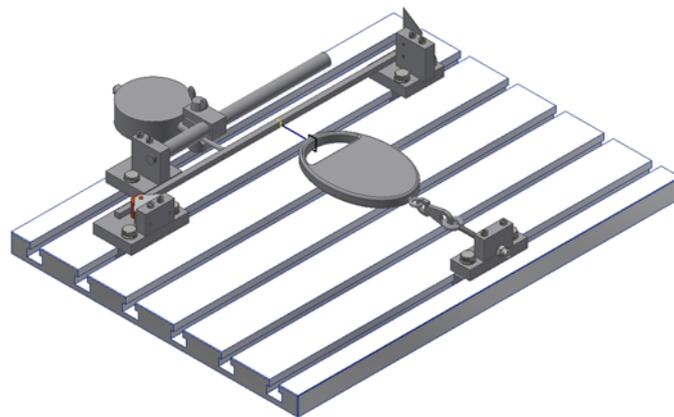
CAD-Darstellung des Prototypens mit Grundplatte, Kraftmesseinrichtung, Wegmessung, Lagerungen und Balken.
